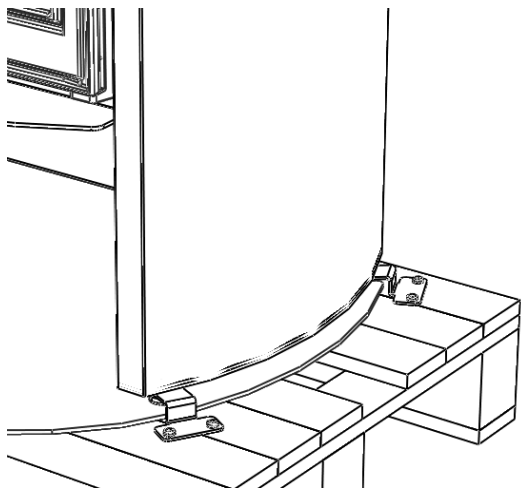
Detalle de las chapas que amarran las patas a la base de madera
